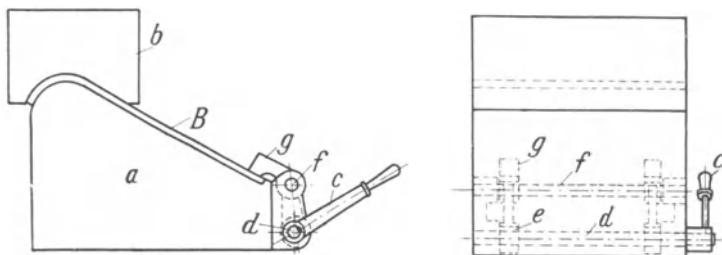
Spannvorrichtung für Bleche unter Pressen.
